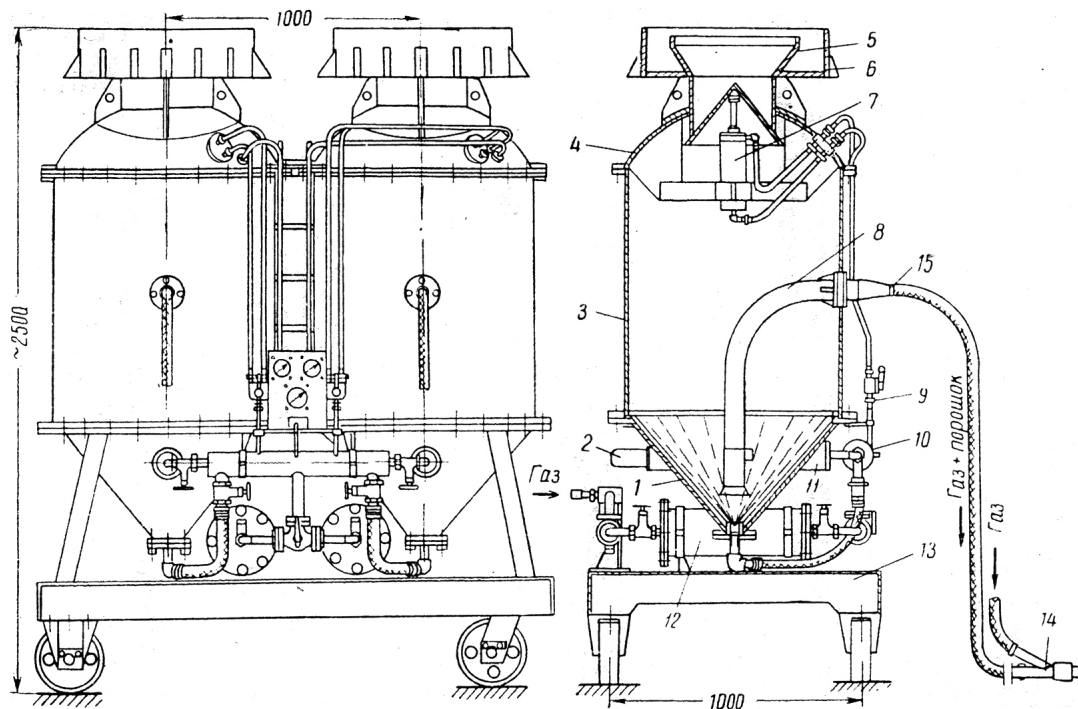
Двухкамерный пневмонагнетатель: 1 – азроднище; 2 – предохранительный клапан; 3 – корпус; 4 – крышка; 5 – загрузочная горловина; 6 – площадка для загрузочного контейнера; 7 – пневматический конусный затвор; 8 – заборная труба для выдачи порошка из пневмонагнетателя в транспортный трубопровод; 9 – трехходовый кран для управления работой конусного затвора и создания начального давления в питателе подачи газа сверху для устранения возможного уплотнения порошка в заборной трубе; 10 – коллектор с запорной арматурой, осуществляющий азрирующую (боковую) и центральную (нижнюю) подачу газа в камеру и подвод газа к трехходовому крану; 11 – патрубков; 12 – абсорбер влаги транспортирующего газа; 13 – передвижная платформа; 14 – сопло, позволяющее очищать транспортный трубопровод от порошка и обеспечивающее возможность безостановочной продувки чистым газом, минуя пневмонагнетатель; 15 – затвор (запорный кран) заборной трубы
